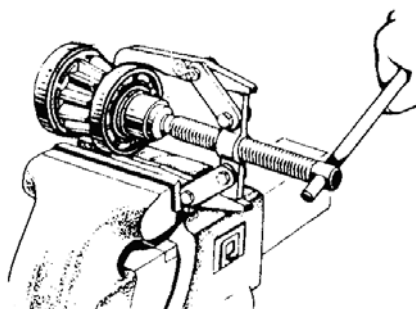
Спрессовка подшипников № 36209КНф и № 208 с ведущей
